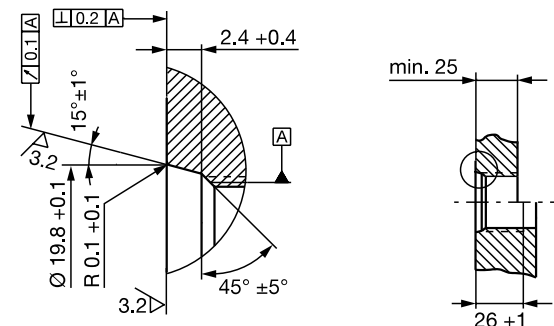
Einschraubloch M18x1.5 nach ISO 6149 O-Ring 15.4x2.1
